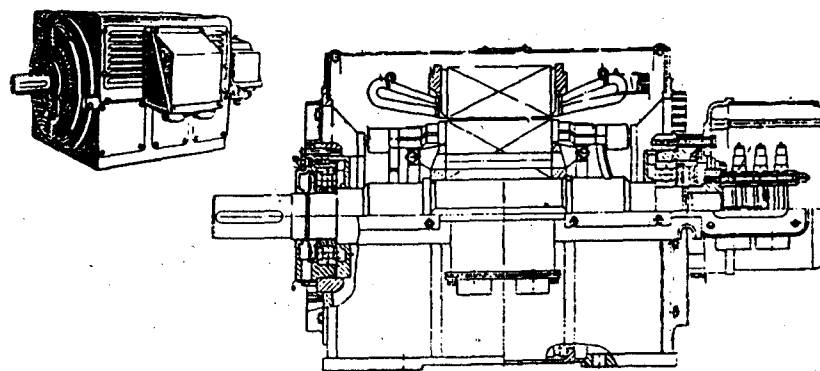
Асинхронный двигатель с фазным ротором серии 4А со степенью защиты IP23 (общий вид и чертеж).
